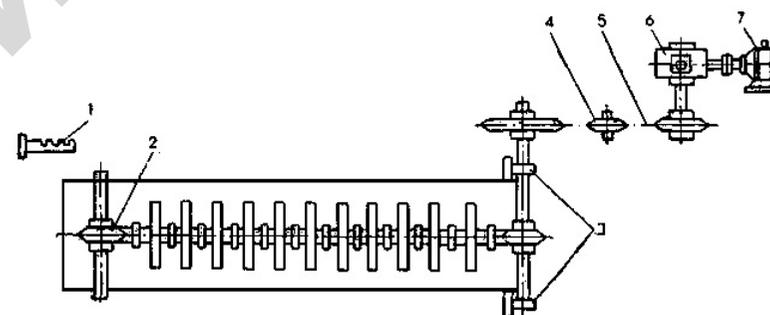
Точки смазки транспортера-раздатчика в кормушках:
